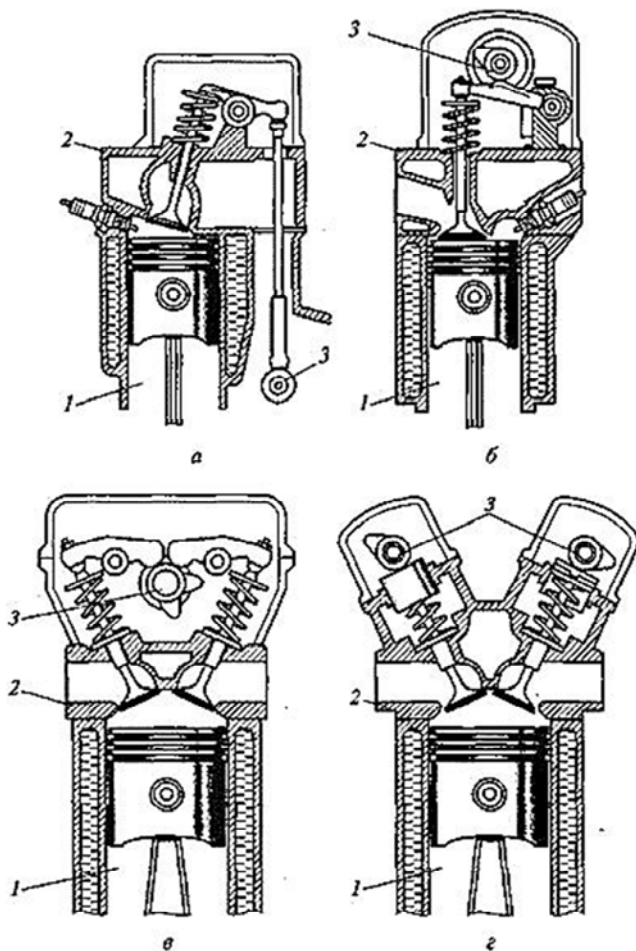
Схемы приводов клапанов газораспределительного механизма:
